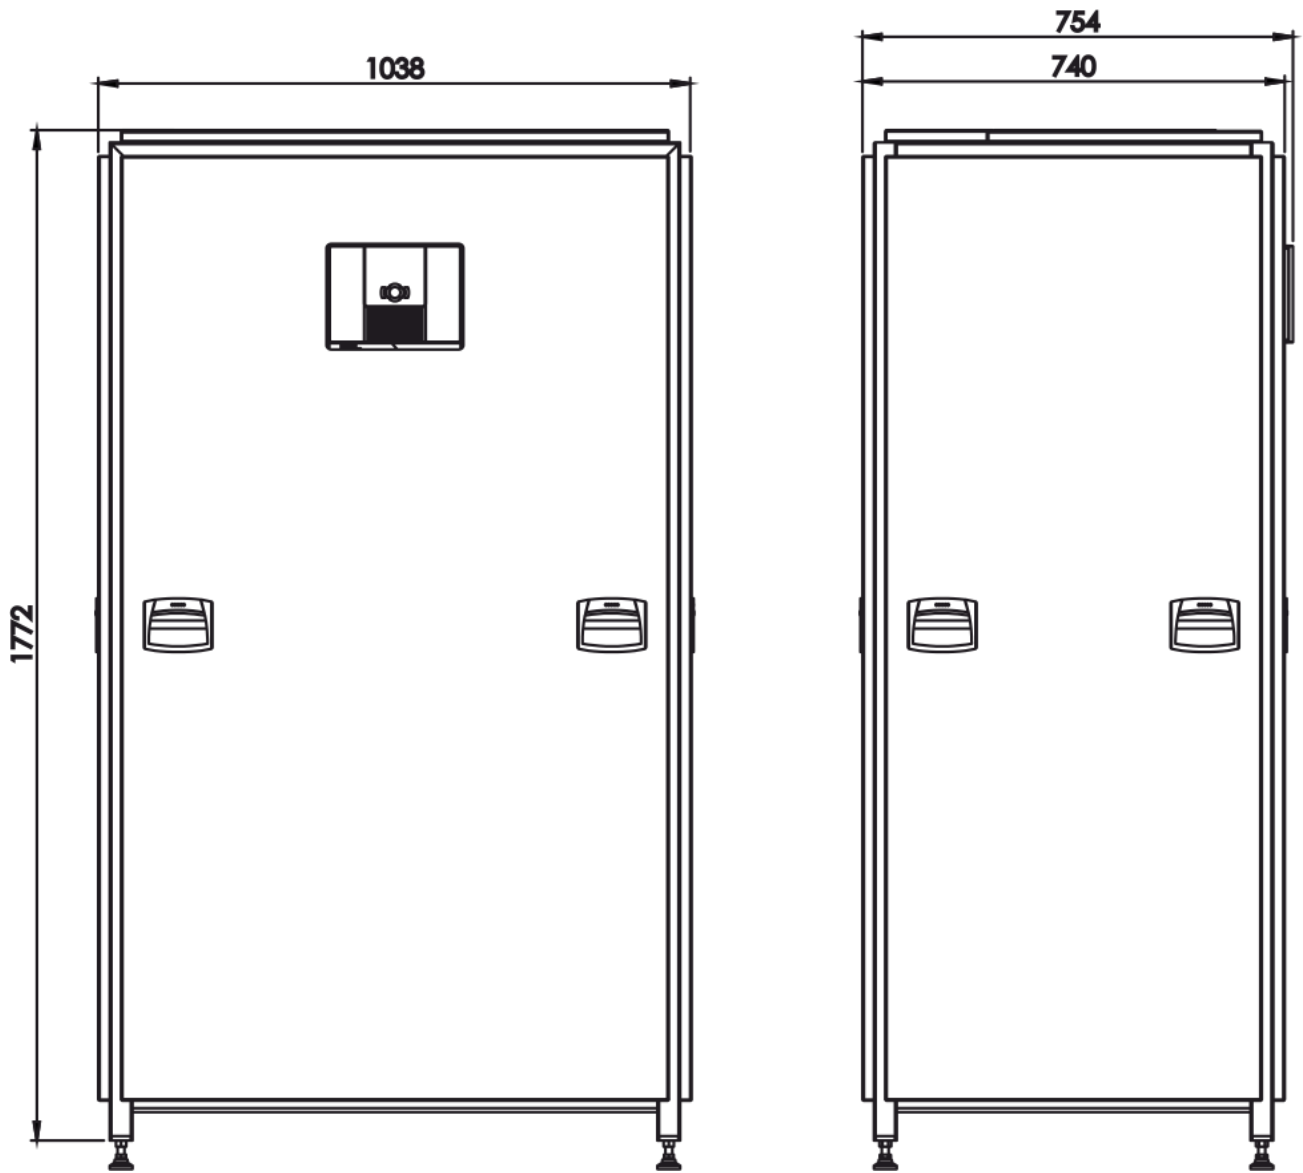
Gehäuse-Außenmaße mit Metallgehäuse
